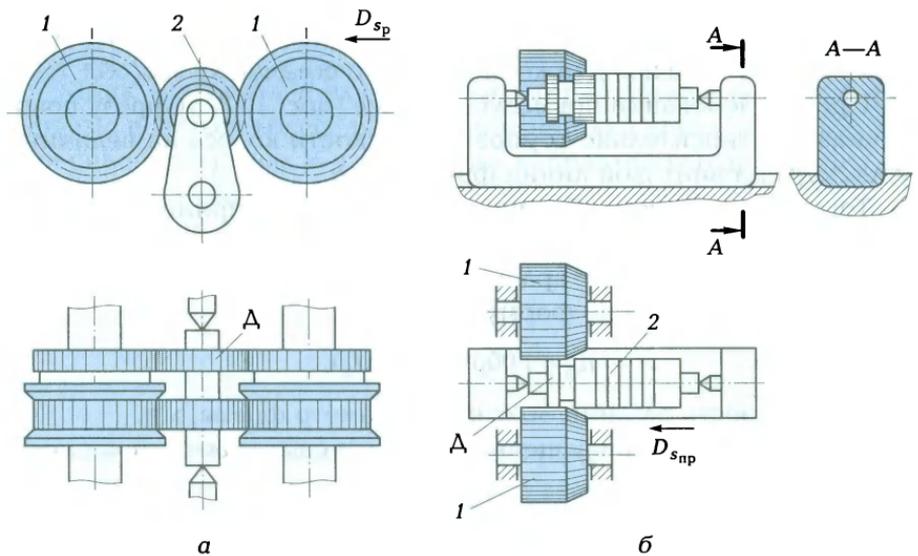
Схемы накатывания цилиндрических колес с поперечной подачей валков (а) и продольной подачей заготовки (б):
